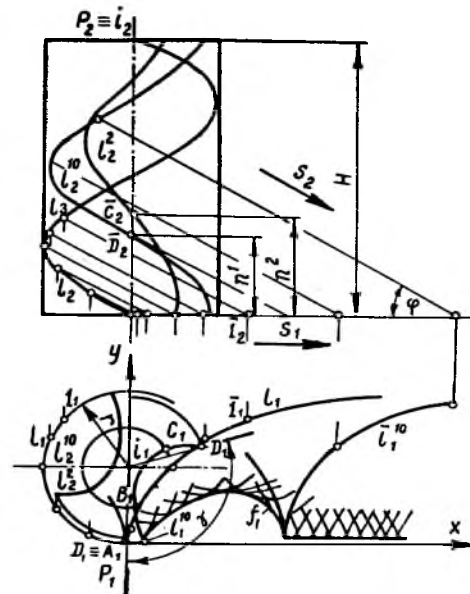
Профілювання вихідної інструментальної поверхні черв'ячних фрез
